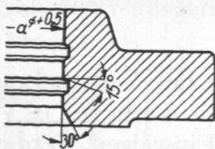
Zylindrische Flanschbohrung mit Abfasung an Walzflanschen.
